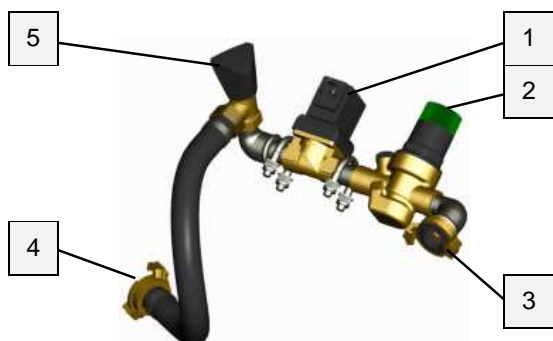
Водопроводная арматура LOTUS XS 00 24 60 57
